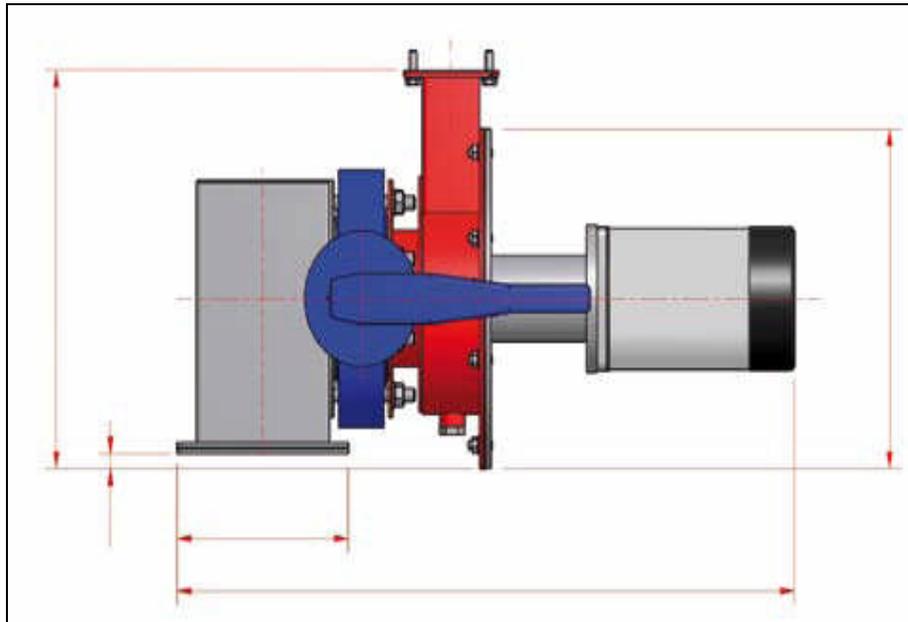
Elektrischer Jet-Thruster mit Ansaugstutzen, Seeventil (blau), Pumpe (rot) und E-Motor (Quelle: Broschüre der Fa. Willdo <http://willdo.nl/images/WillDo%20Jetthruster/WillDo3luikEN.pdf>).
